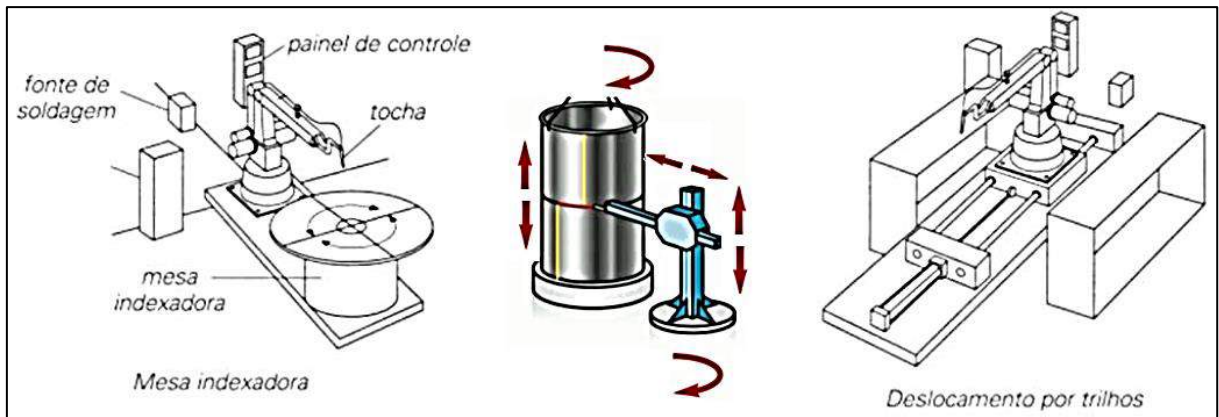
Manipuladores de Soldagem, adaptado de SENAI-SP, 1997.
